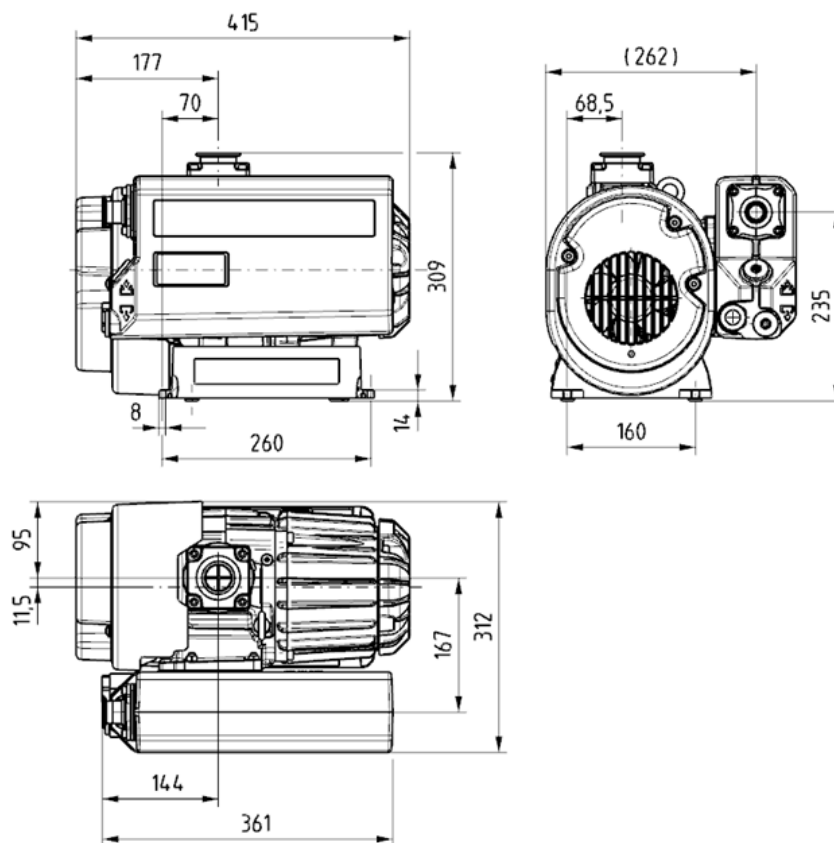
Dimensions de la SmartVane 55 avec séparateur de 1 l
